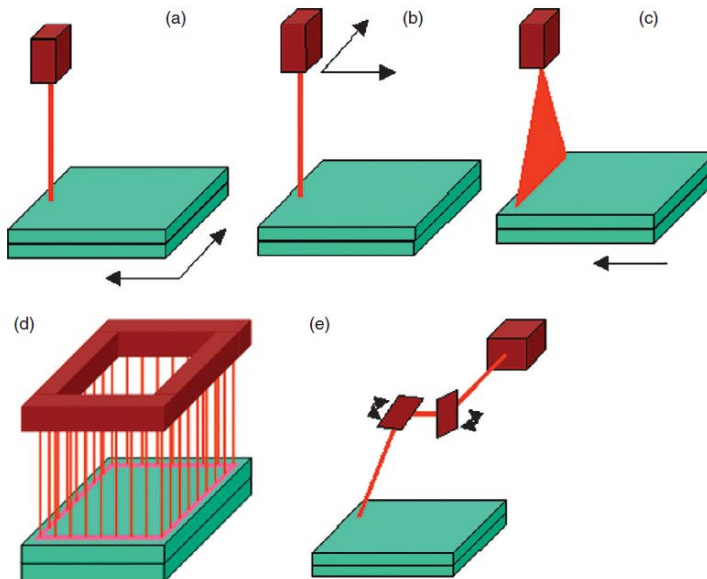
Métodos de soldadura láser: (a) pieza móvil, (b) láser móvil, (c) láser de cortina, (d) soldadura simultánea y (e) láser de escáner (Troughton, 2008).
